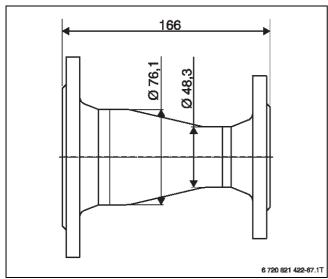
Übergangsstück DN 65/PN 6 – DN 40/PN 6 (Maße in mm)
